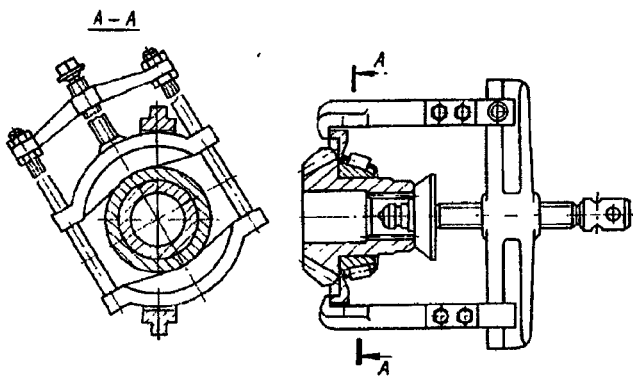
Снятие внутренних колец подшипников ведущих зубчатых колес съемником
